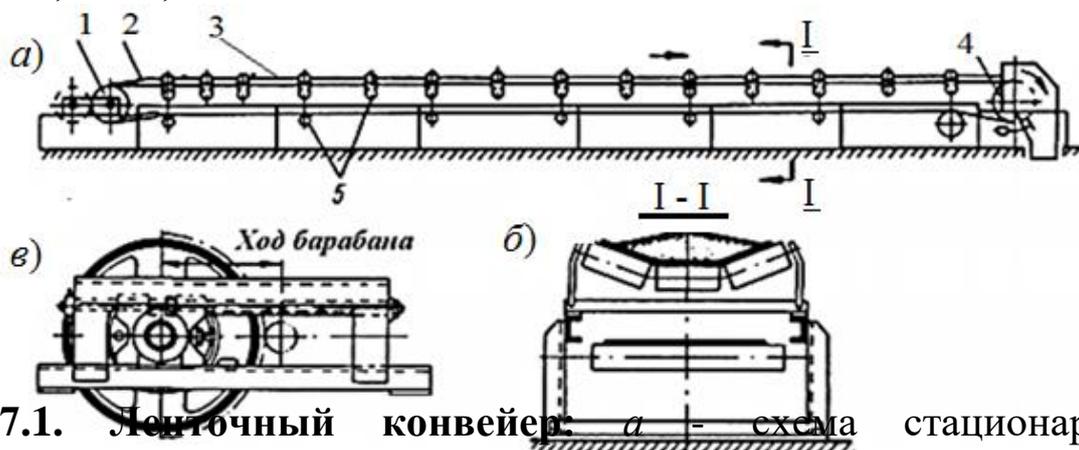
Ленточный конвейер: а - схема стационарного горизонтального конвейера; б - поперечный разрез; в - натяжное устройство; 1 – натяжной барабан; 2 – лента; 3 – загрузочный бункер; 4 – приводной барабан; 5 – роликовые опоры.
